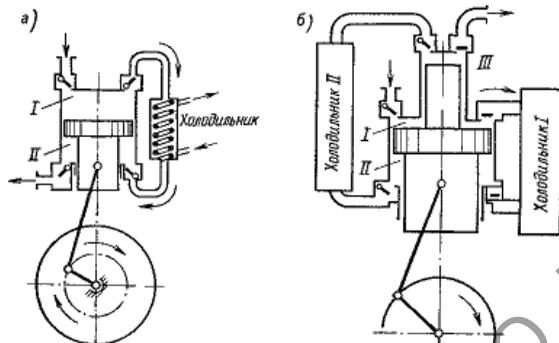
Схемы компрессоров с дифференциальным поршнем:
